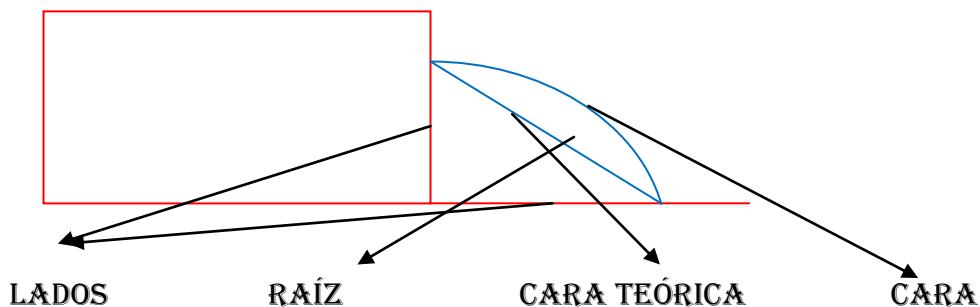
Soldadura de Filete<sup>2</sup>
